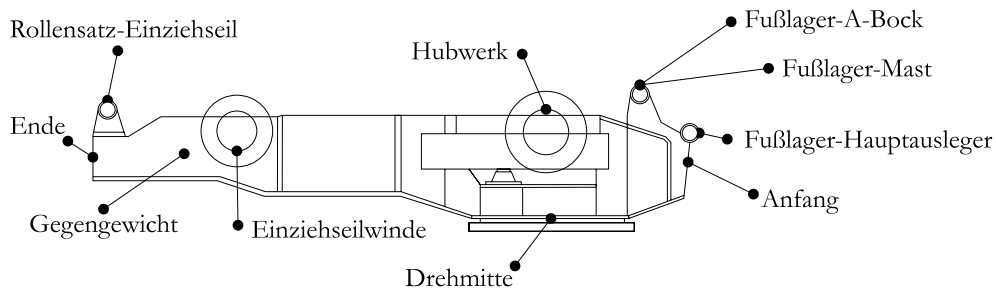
Anschlüsse des Bauteilprototypen Oberwagens
